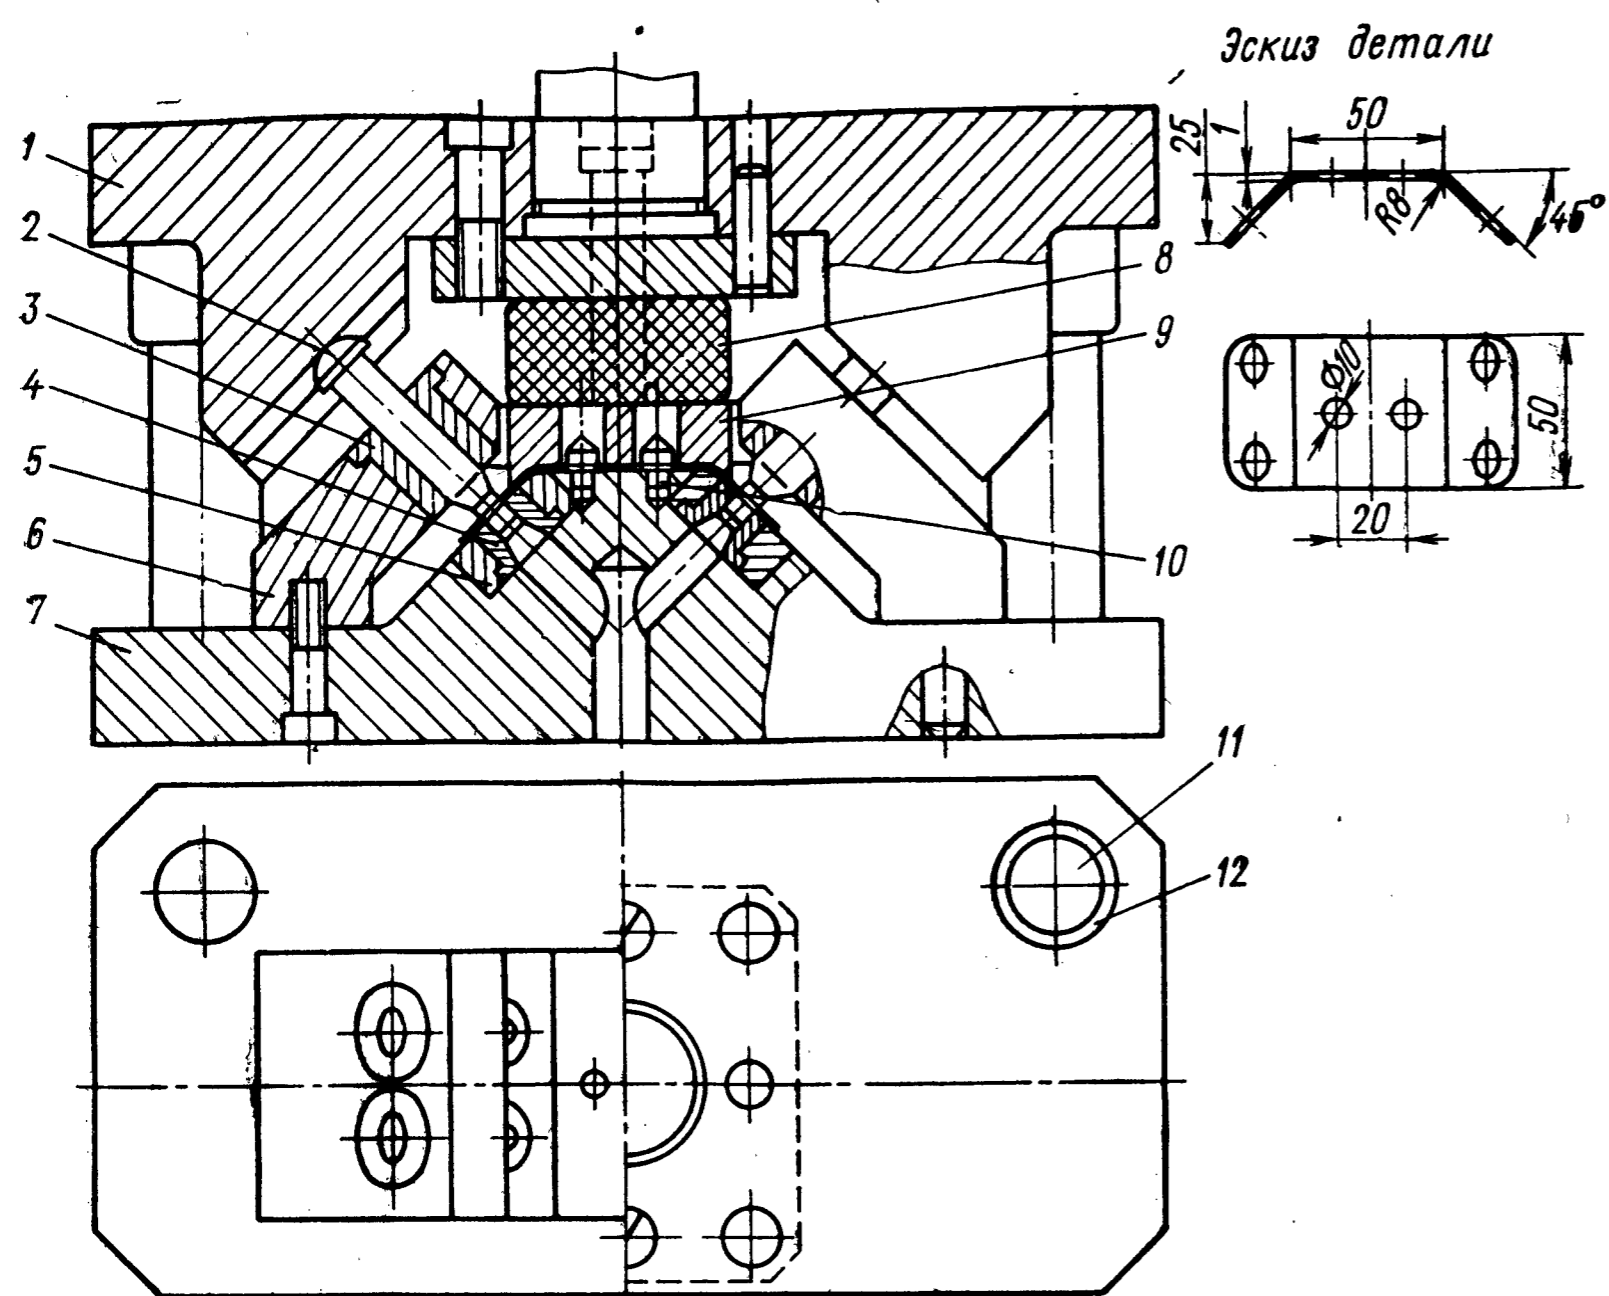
Штамп для пробивки отверстий, расположенных под углом друг к другу
